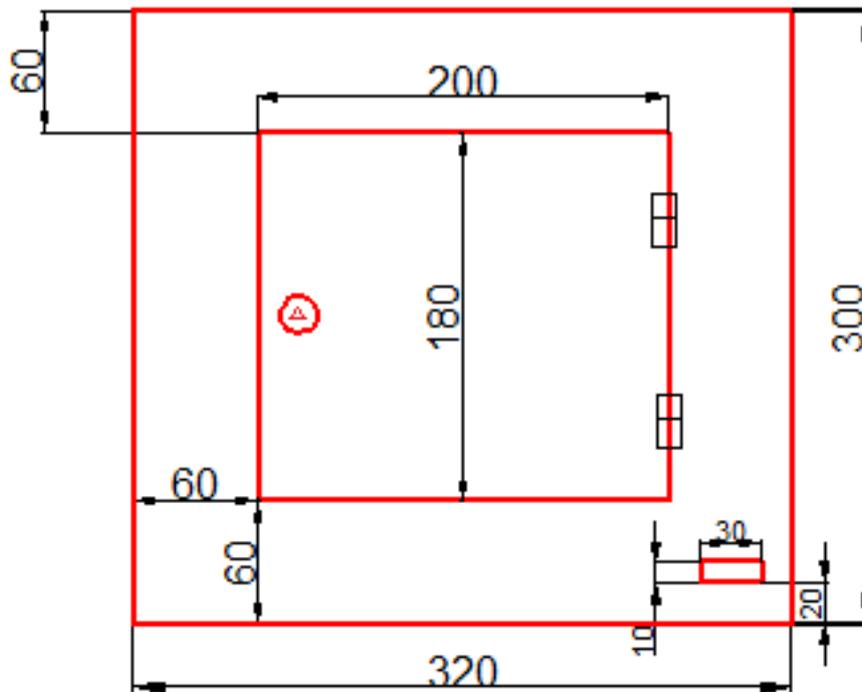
3 Diseño de la vista posterior de la estructura. Diseño en AutoCAD de la vista posterior del módulo PLC
